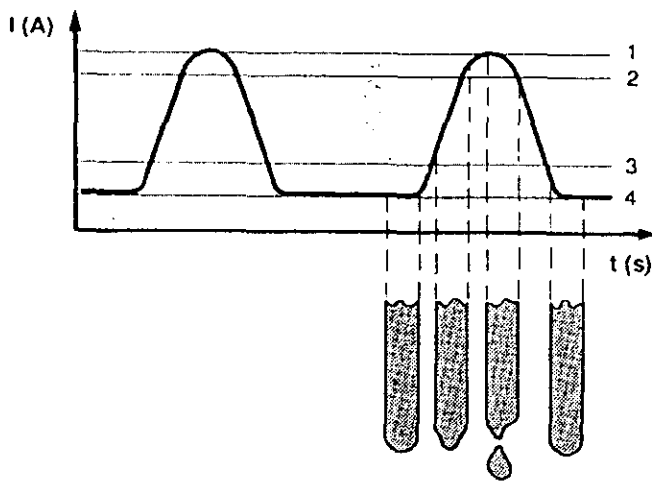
Descripción de la soldadura de arco pulsado.
